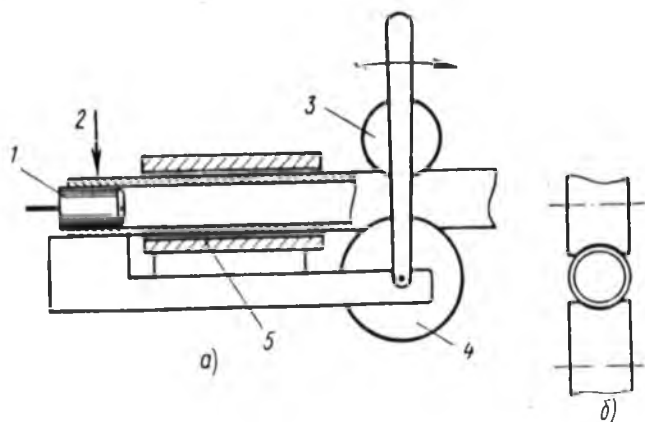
Приспособление для гибки волноводов прокаткой между роликами:
